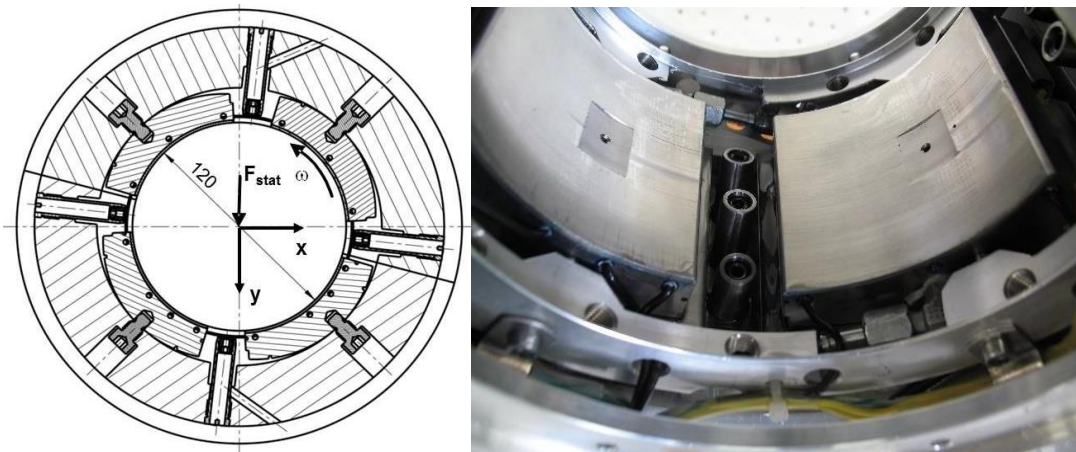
Конструкція підшипника ковзання з поворотними сегментами [18]
